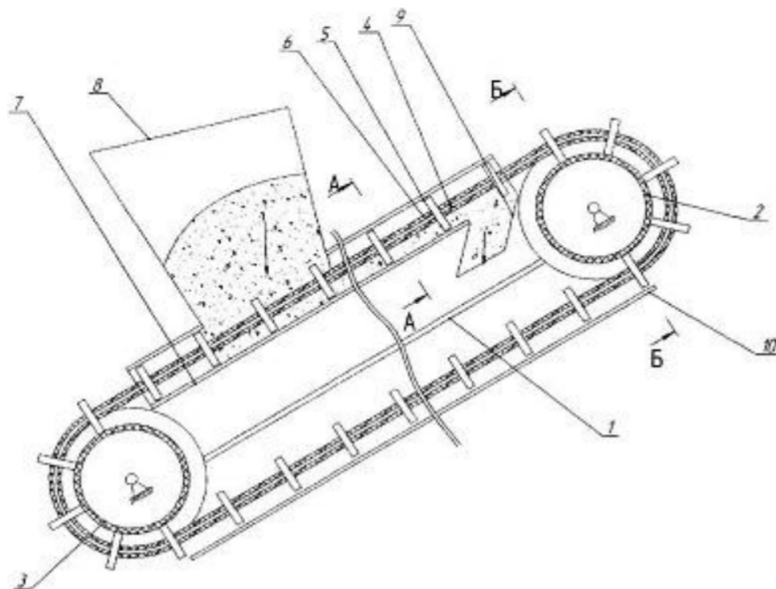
Загальний вигляд скребкового транспортера
